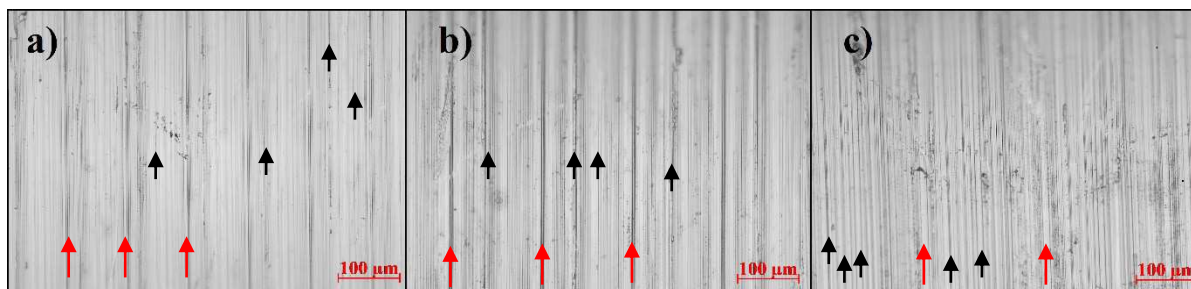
Imagens das superfícies torneadas: a) Ra-torneado = 0,54 μm , b) Ra-torneado = 0,80 μm e c) Ra-torneado = 1,17 μm .
